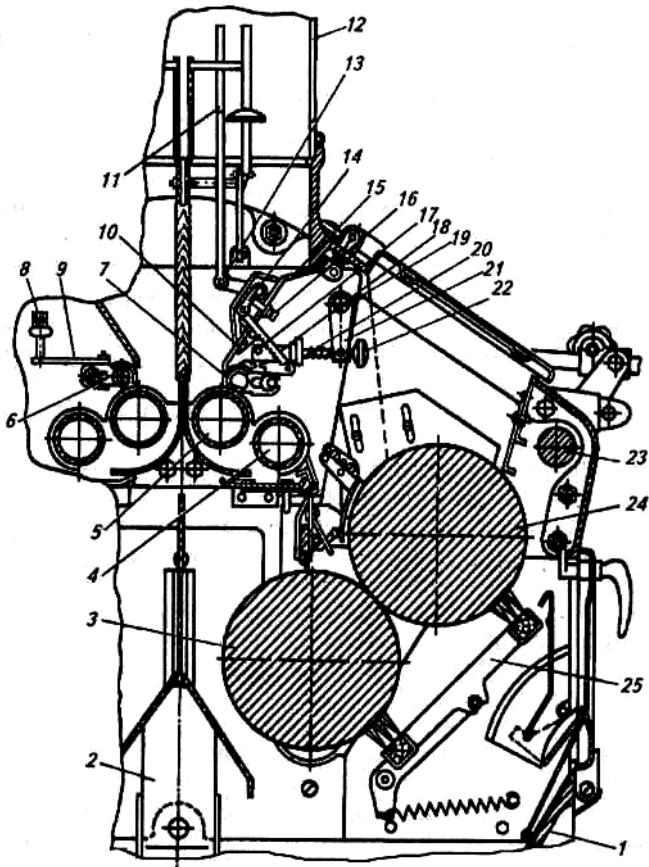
Вальцовый станок 3М2: 1 - станина; 2 -аспирационное устройство; 3, 24 -медленновращающийся и быстровращающийся вальцы; 4, 5 - распределительный и дозирующий валики; 6, 13, 14, 21- рычаги; 7 - секторная заслонка; 8 - регулировочный винт; 9 - планка; 10 - пружина; 11 - датчик питателя; 12 - питающая труба; 15 - клапан; 16 - винт; 17 - тяга; 18 - серьга; 19 -вал; 20 - амортизационная пружина; 22- винт; 23 - эксцентриковый вал; 25 - щетка.
